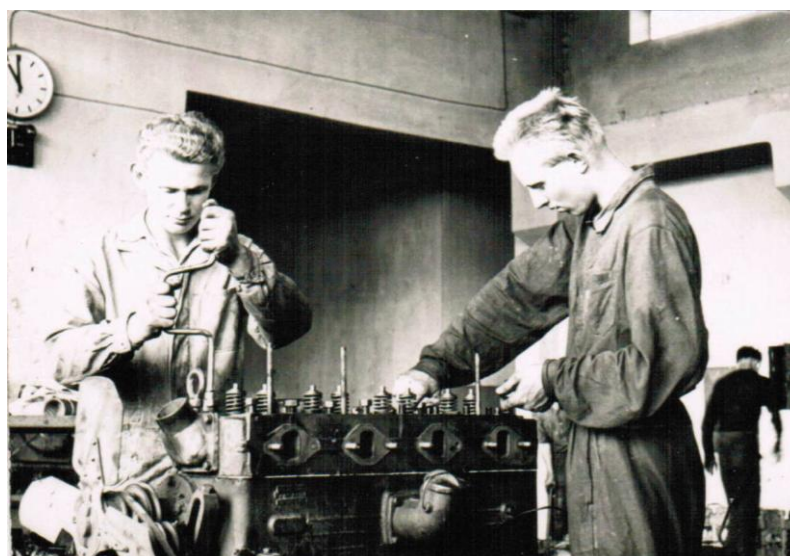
Oprava zemědělské techniky – archiv SOŠ a SOU Písek
